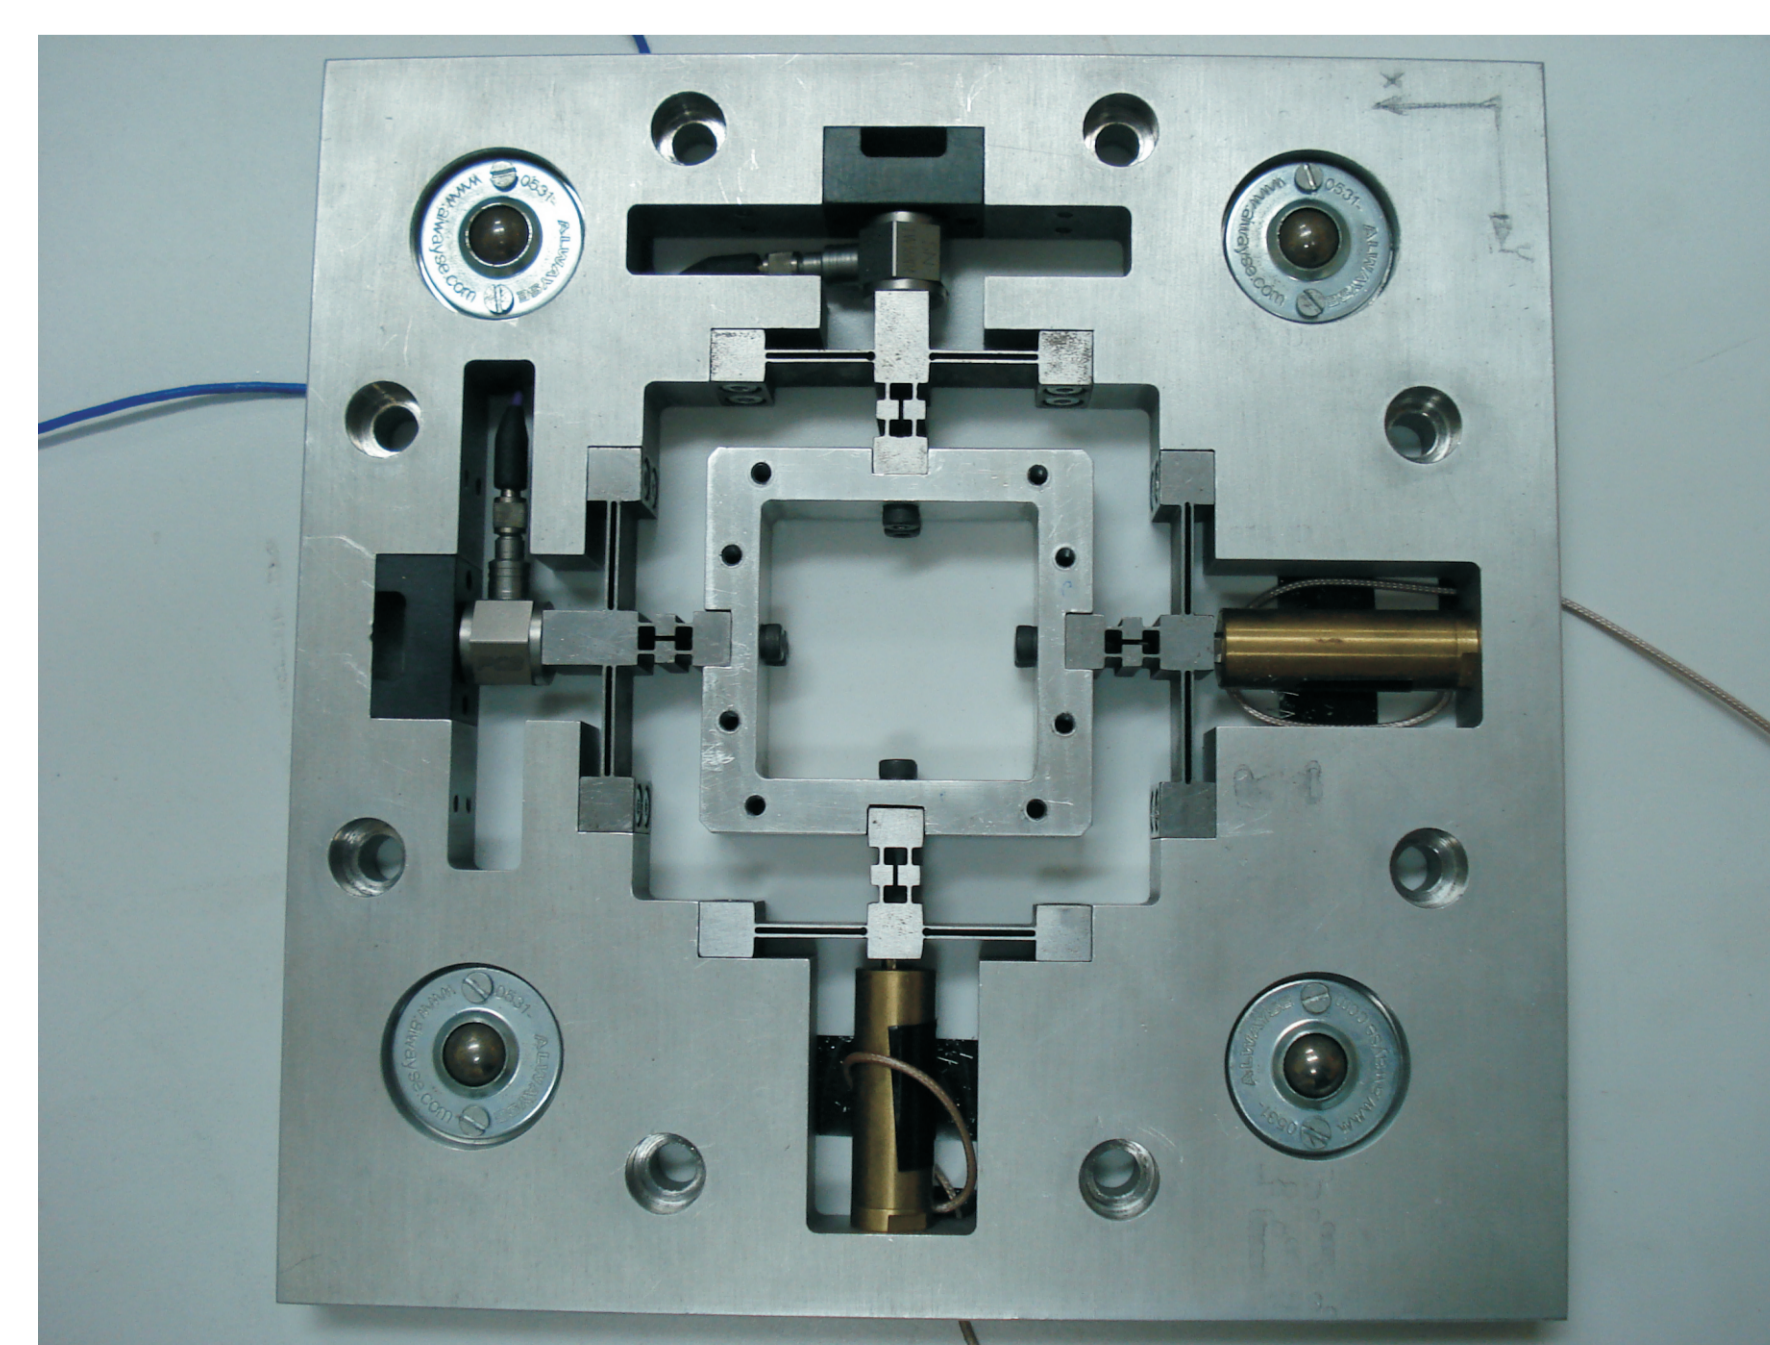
Stanowisko testowe aktywnego uchwytu obróbkowego
